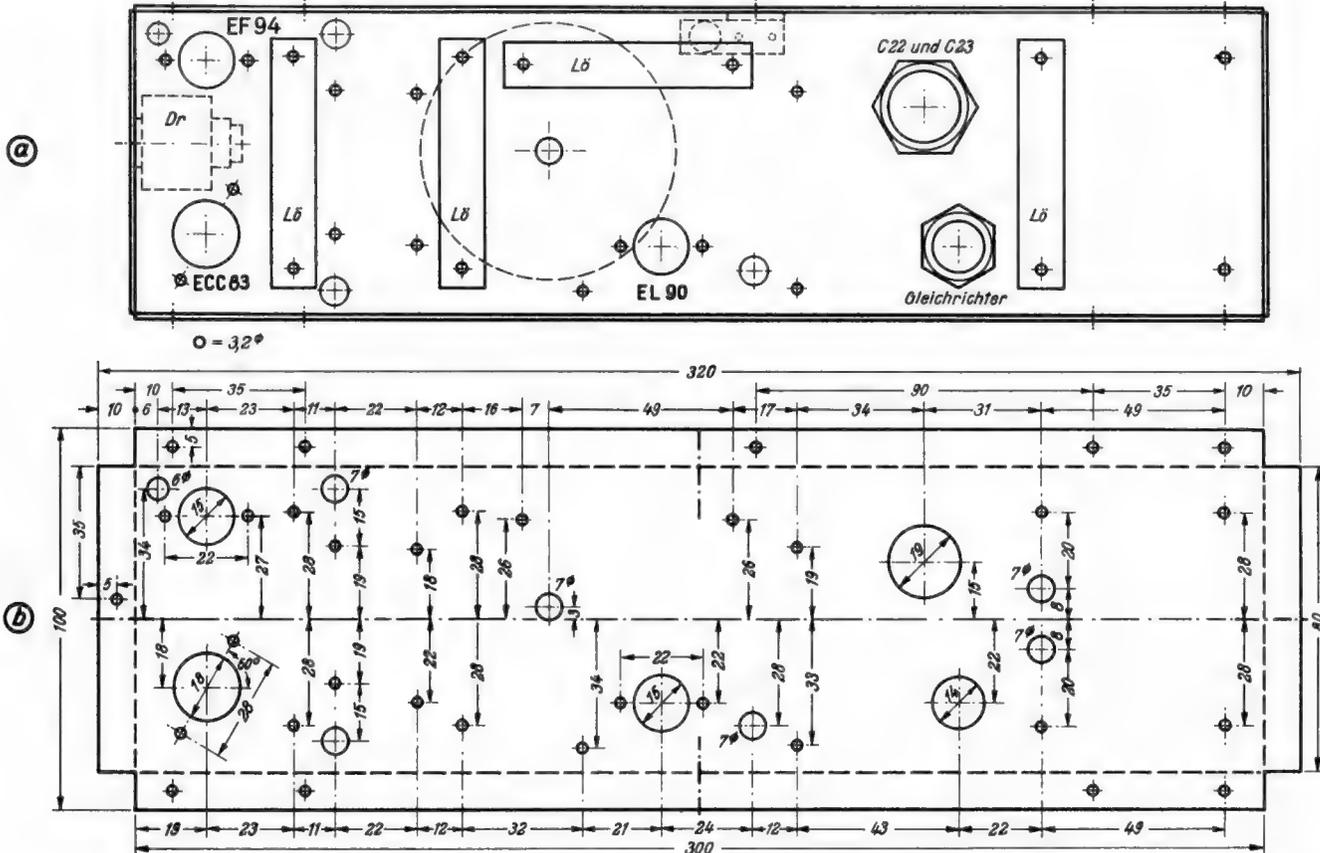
Maßskizze des Chassis von der Frontplattenseite aus gesehen. a = bestückt; b = gebohrt; L6 = Lötösenstreifen
